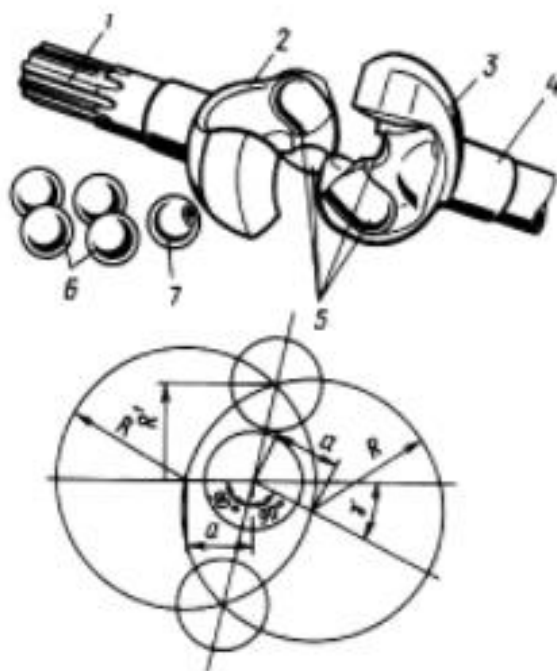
Шариковый карданный шарнир с делительными канавками (типа “Вейс”): 1 и 4 – валы; 2 и 3 – кулаки; 5 – канавка; 6 – шарики; 7 – центрирующий шарик
